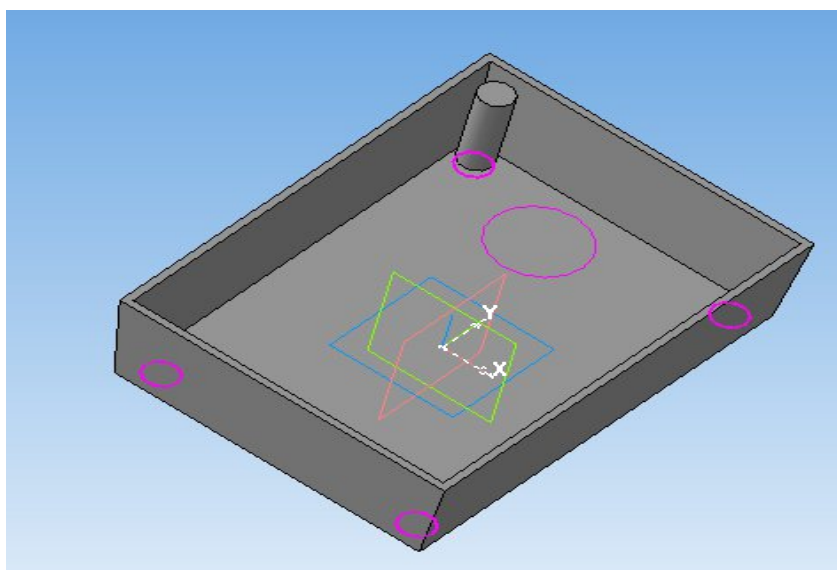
Объемная заготовка крышки корпуса с одной стойкой
